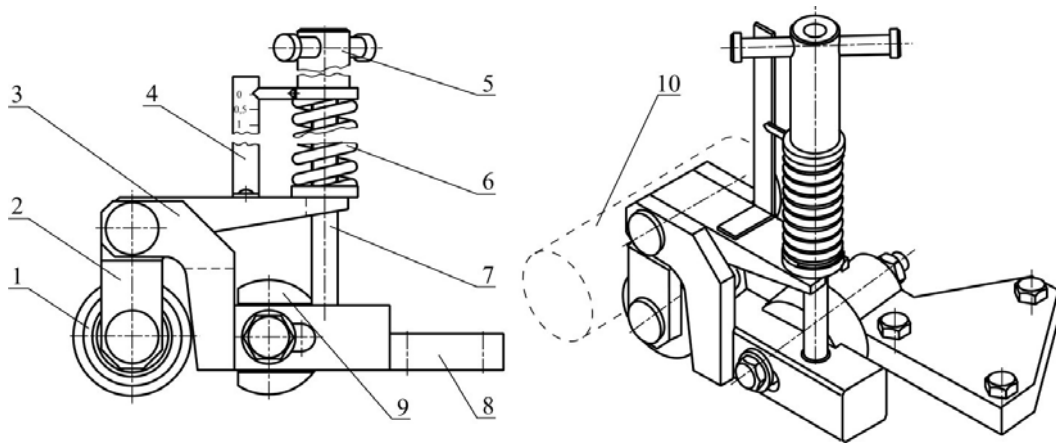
Схема одноролікового пристрою: 1 – ролик; 2 – коромисло; 3 – важіль; 4 – шкала; 5 – гайка; 6 – пружина; 7 – шпилька; 8 – пластина; 9 – втулка; 10 – деталь, поверхня якої підлягає відновленню
